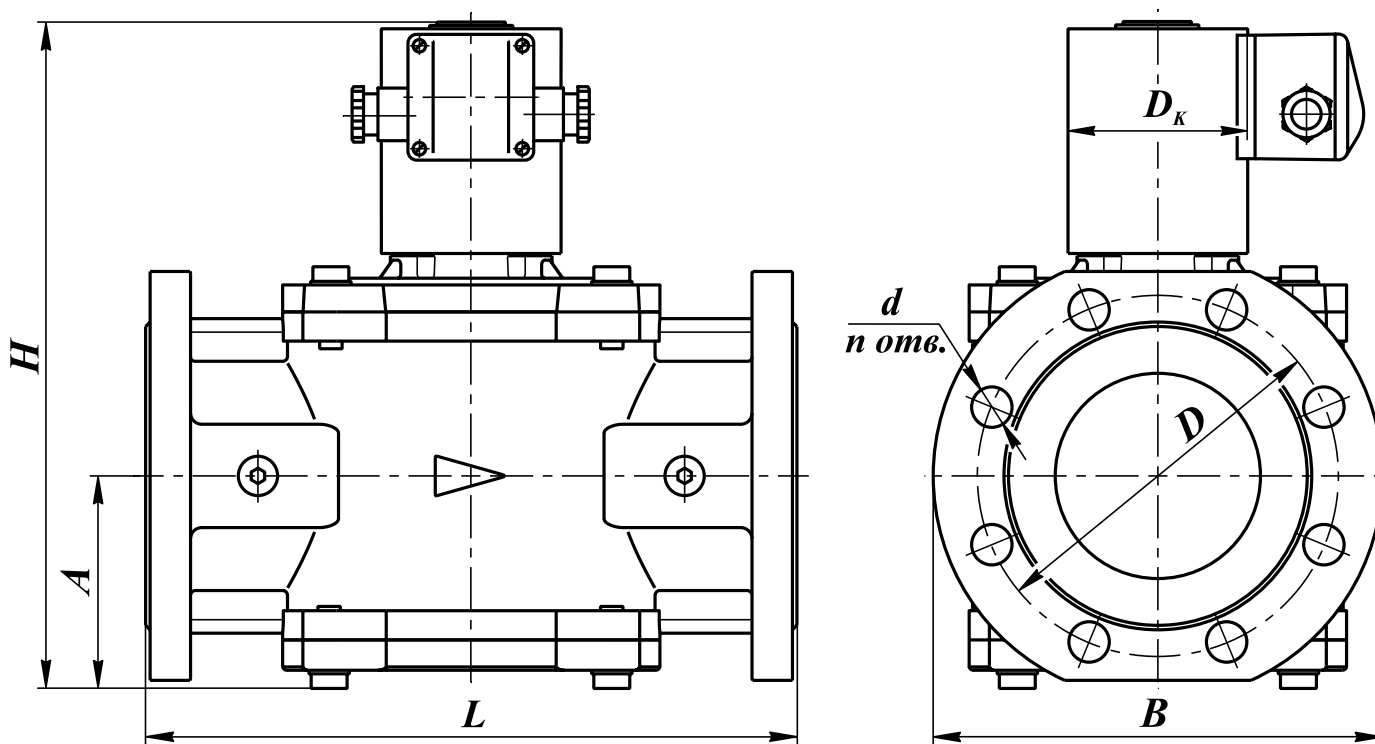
Клапаны на DN 50 - 100 фланцевые (исполнение: с присоединительными фланцами PN16)
